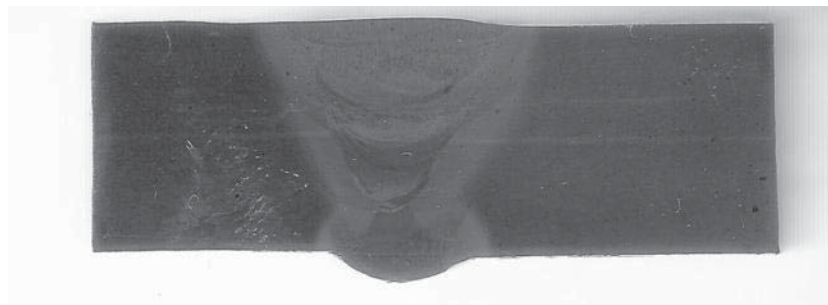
Soldadura de acero al carbón con electrodo revestido.
